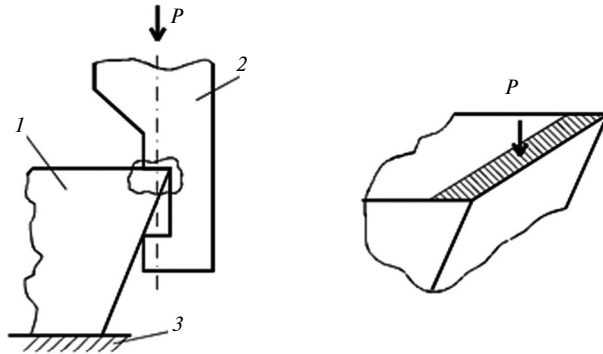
Схема консольного изгиба неперетачиваемых режущих пластин: 1 – нагружающий элемент; 2 – режущая пластина; 3 – опора.
